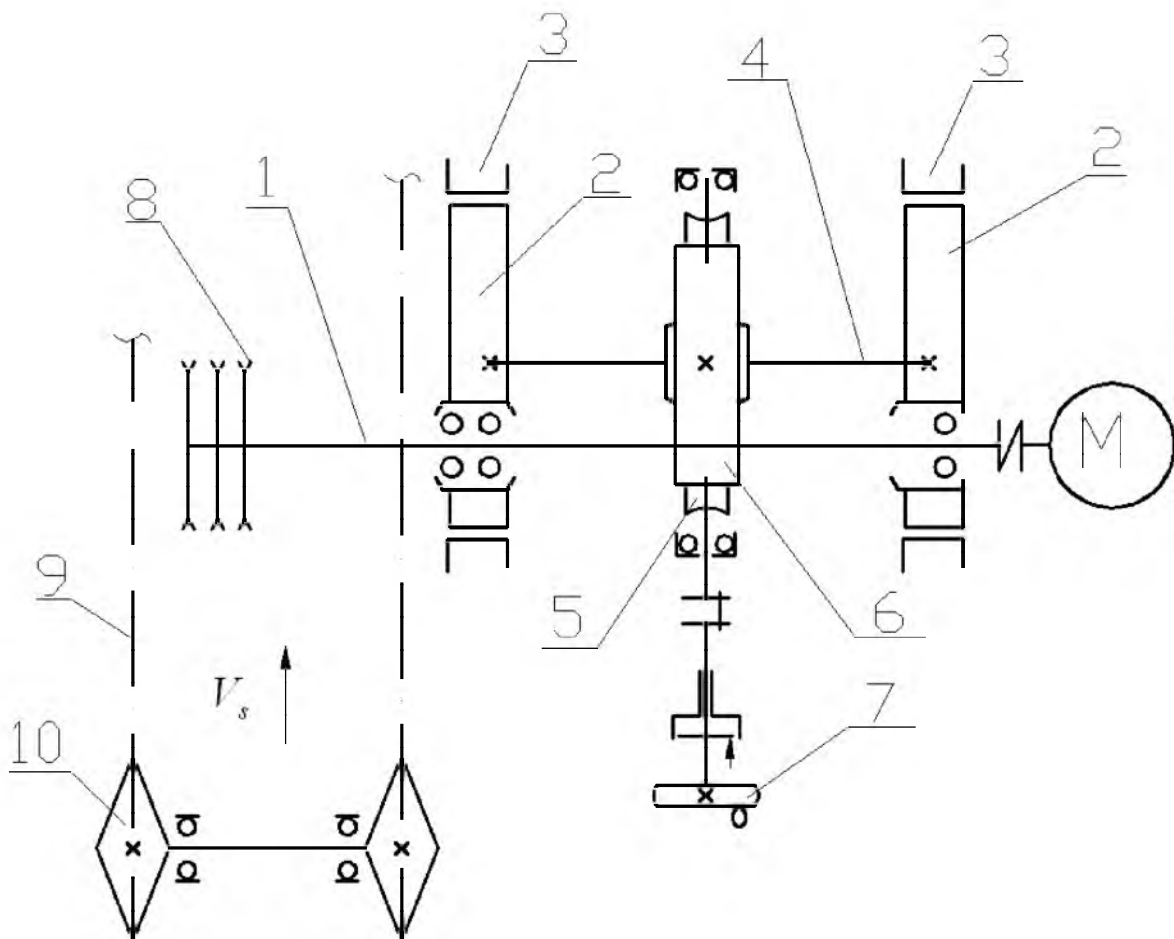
Существующая схема управления положением пильного вала станка ЦДК 5
